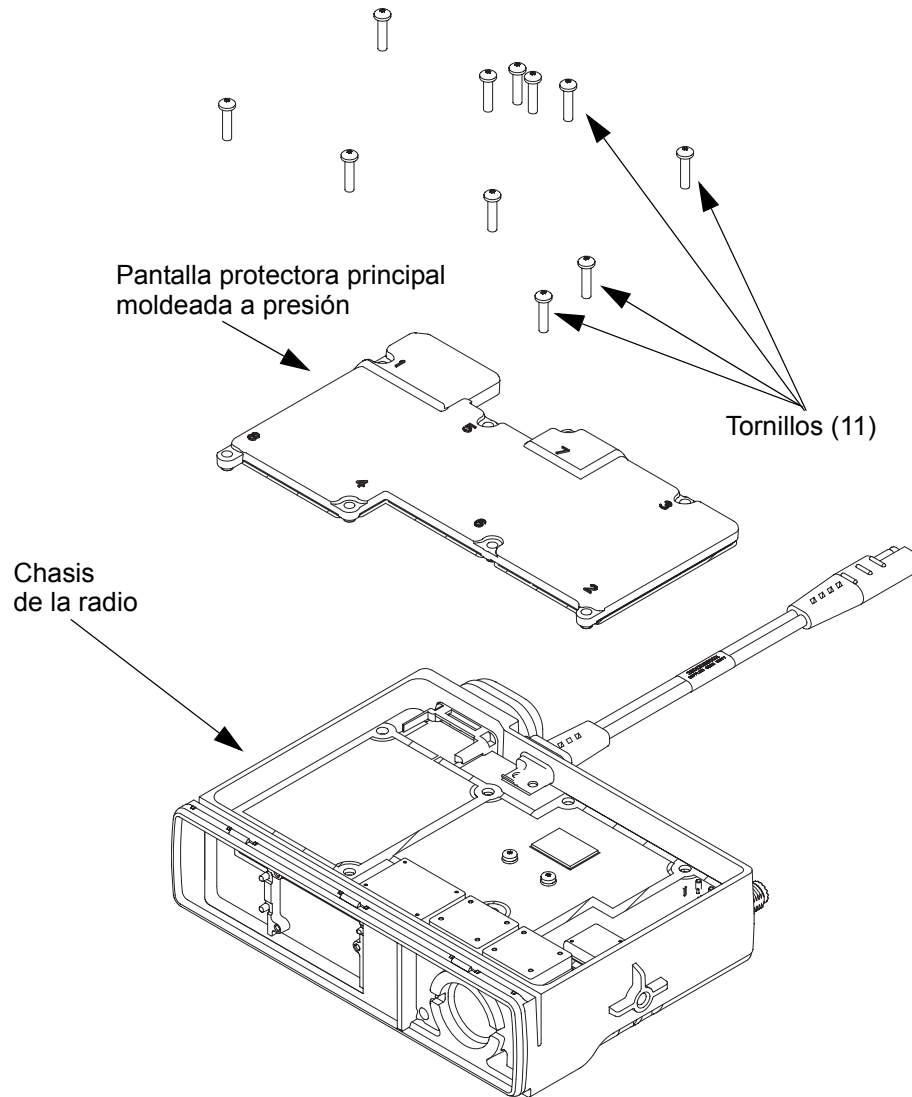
Extracción de la pantalla protectora principal moldeada a presión
